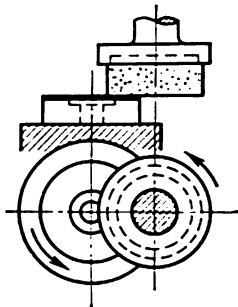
Rectification d'un plan par la face d'une meule boisseau sur une machine à table pivotante
